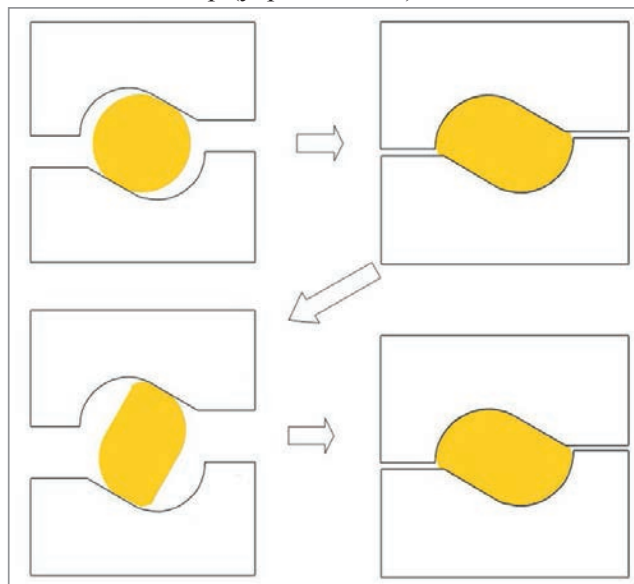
Схемаковки (протяжки) заготовок в бойках новой конструкции
